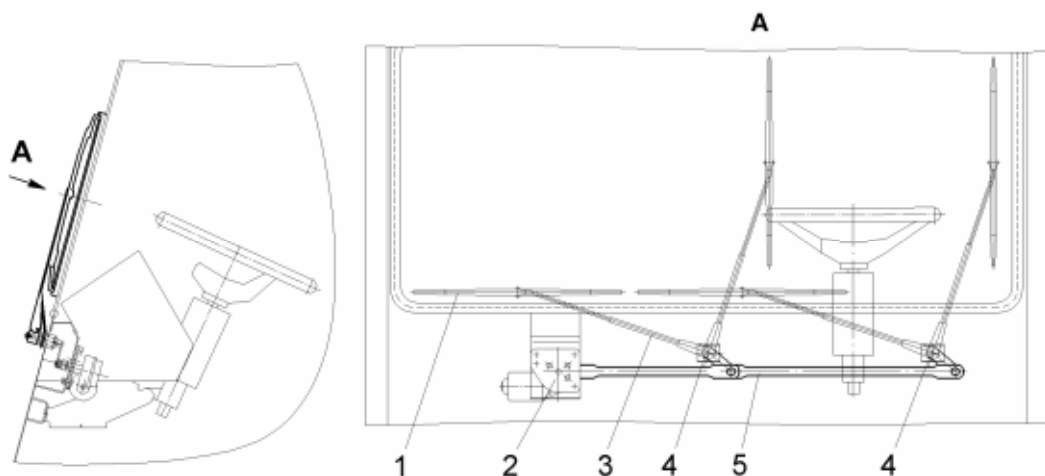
Снятие и установка рычага и щетки стеклоочистителя:
